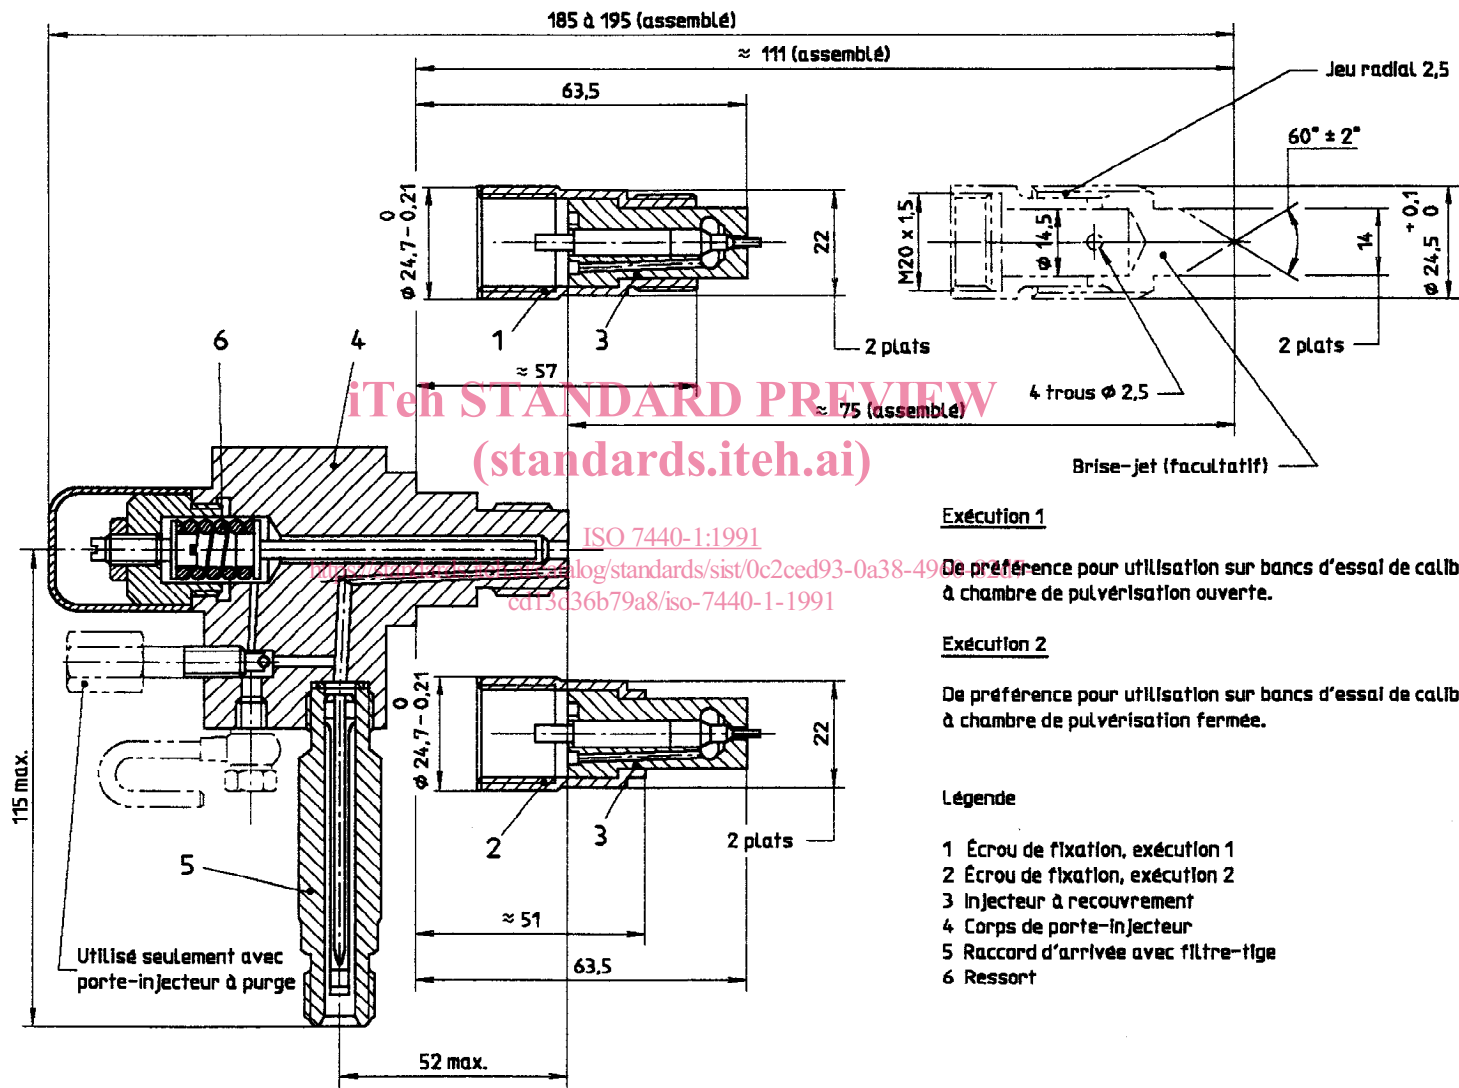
Ensemble porte-injecteur et injecteur avec injecteur à recouvrement
